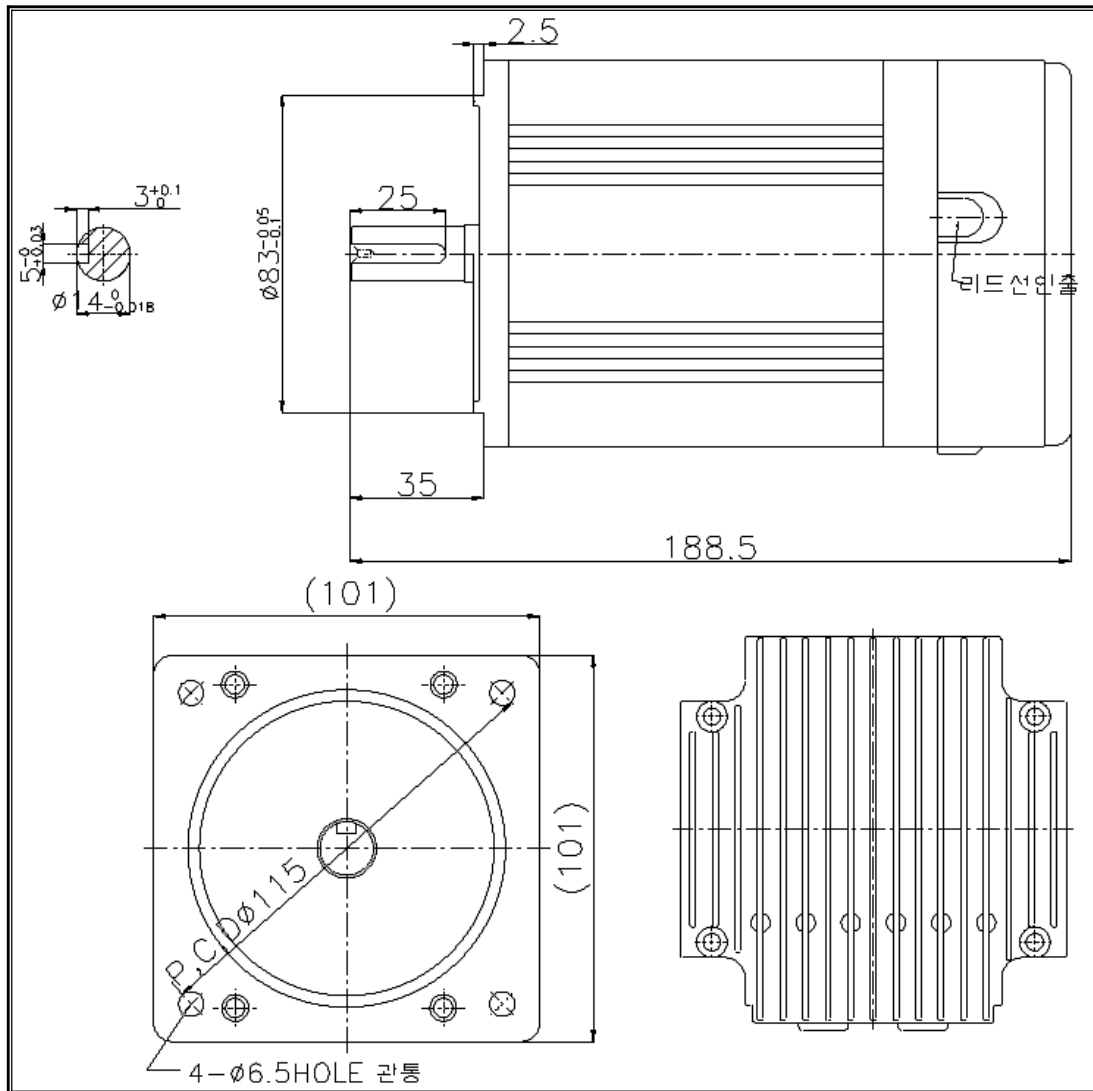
BLDC MOTOR 외형도(400W TM10-A0423,A0433시리즈, 750W TM-10-A0753시리즈)
